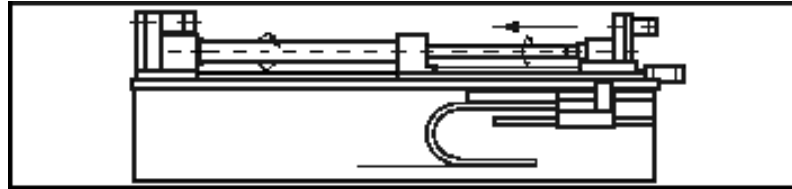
Universal-ELB-Tiefbohrmaschine [4]
